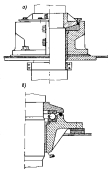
Опорно-упорный подшипник баллера: а — с подшипником скольжения; б — с подшипником качения
